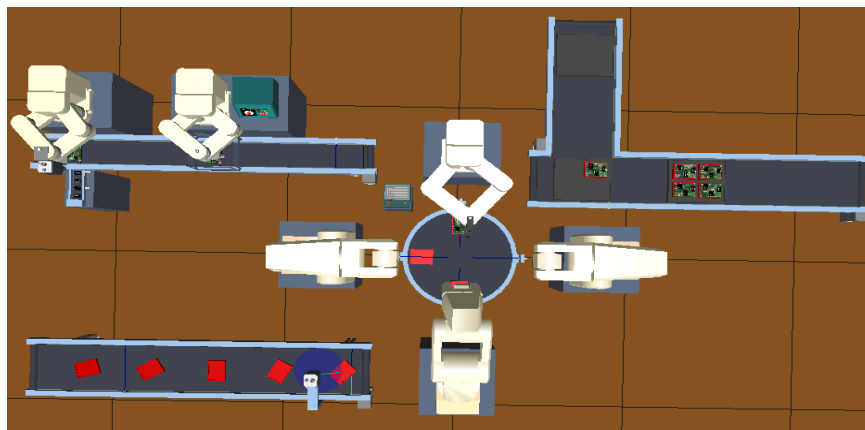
Simulación del sistema del proceso del Ensamblaje y Soldadura
